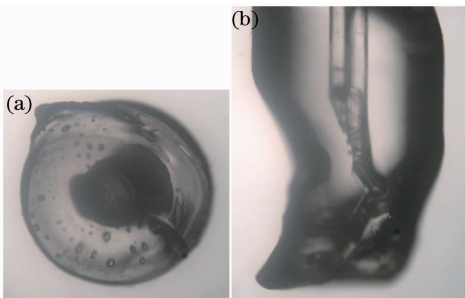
焊接导致膜片烧毁(a)和锥形口变形(b)
